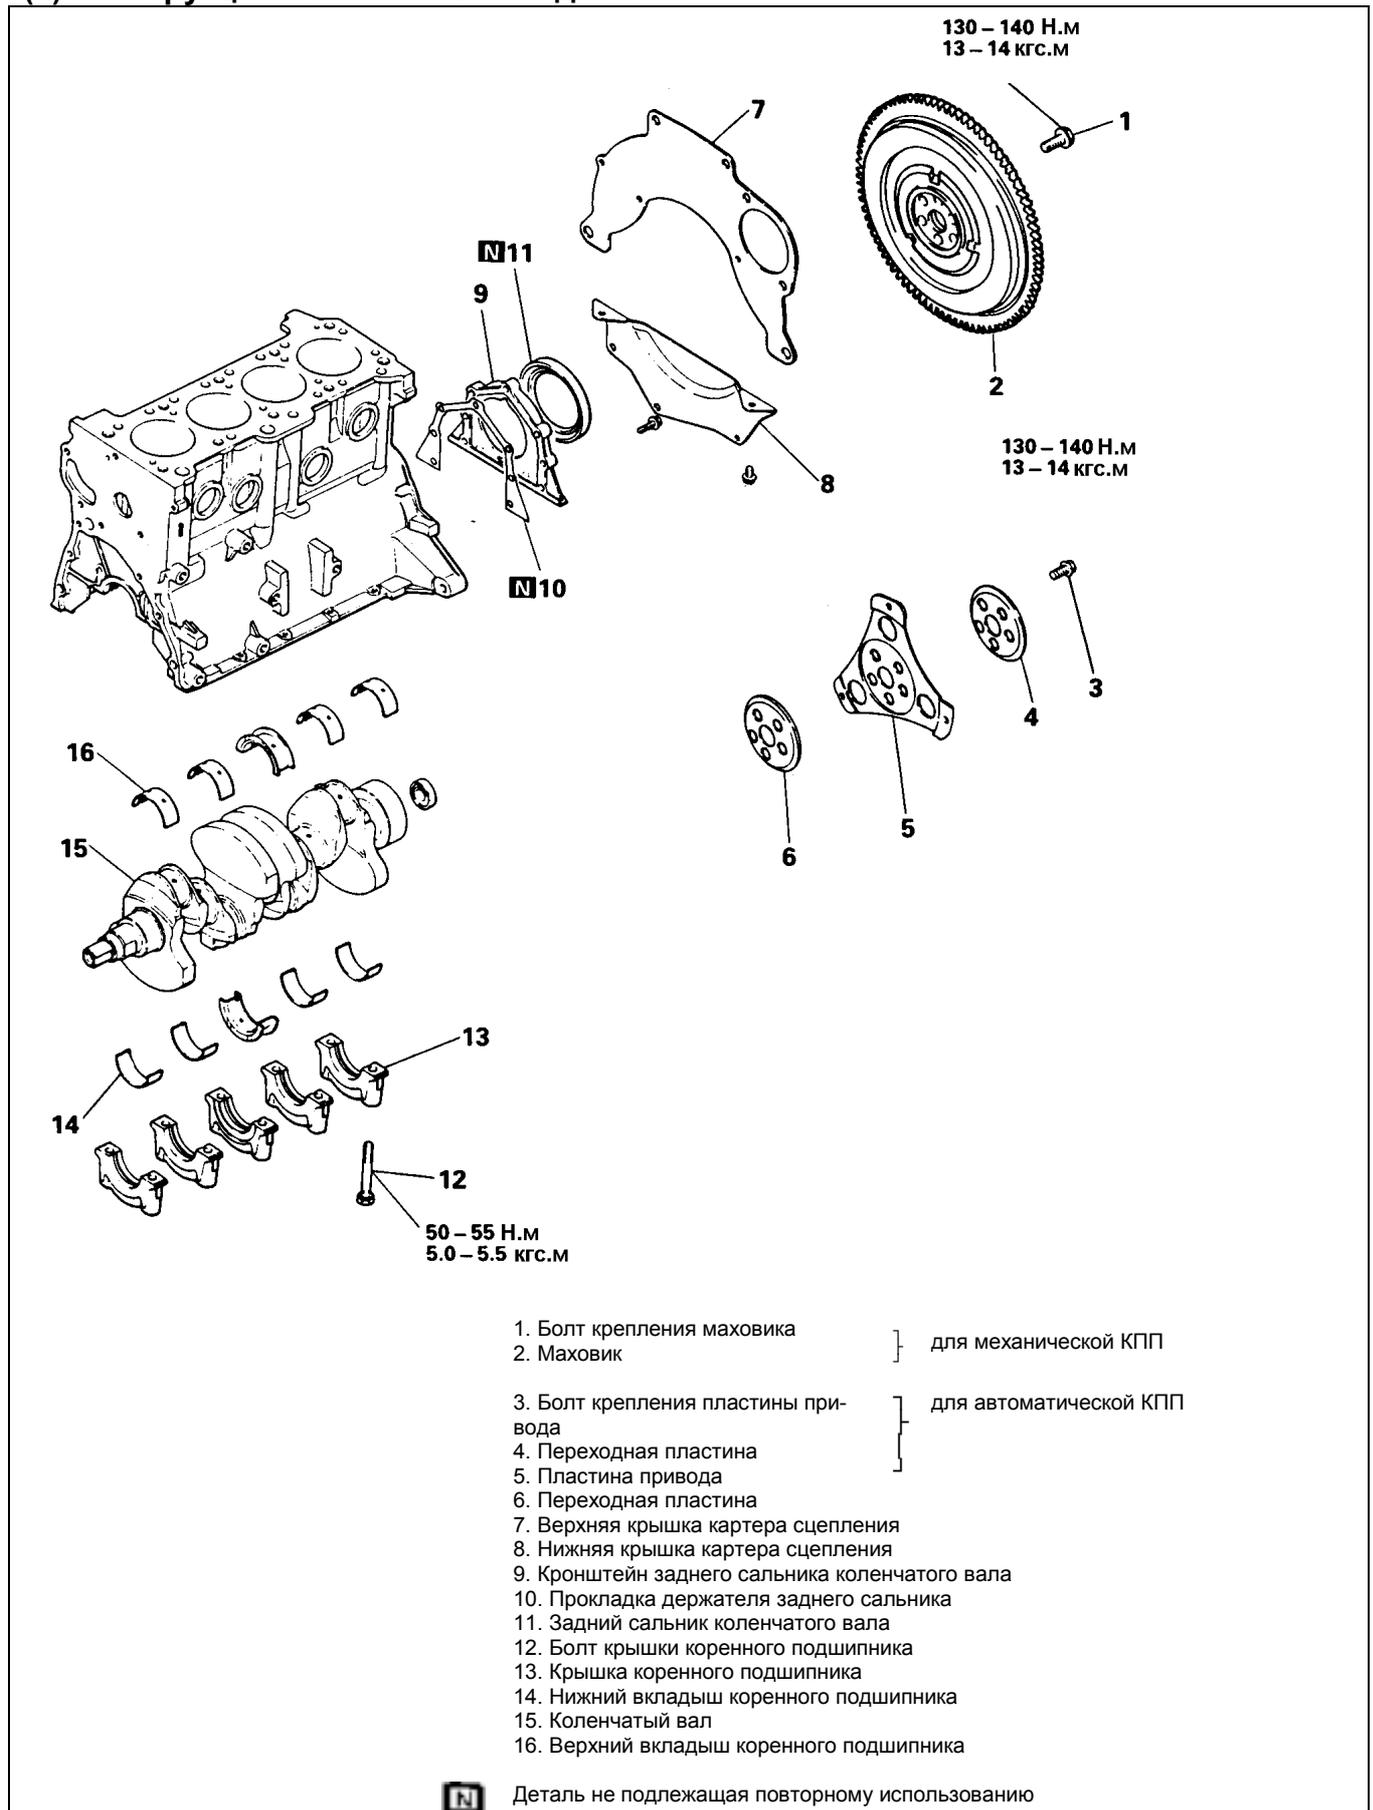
Коленчатый вал, маховик и ведущий диск
